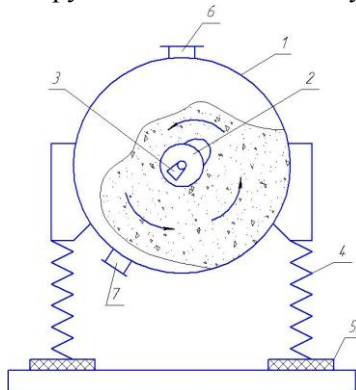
Схема трубчастого віброзмішувача: 1 – корпус; 2 – труба;
